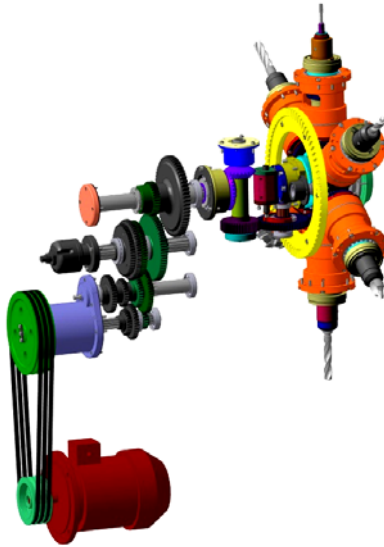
Кінематична схема приводу головного руху з шестишпindelною револьверною голівкою
